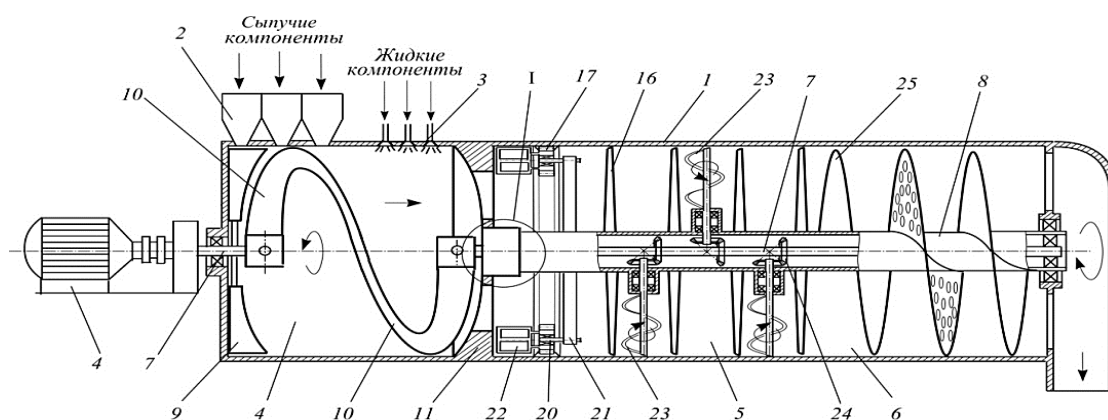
Смеситель с Z-образным рабочим органом. Общий вид. 1 – корпус; 2 – загрузочные патрубки; 3 – форсунки; 4–6 – камеры; 7, 8 – быстроходный и тихоходный валы; 9 – очищающие лопасти; 10 – z-образные лопасти; 11 – опора; 16 – конусообразные лопасти; 20 – ось; 21 – стойка; 22 – рамные мешалки; 23 – спирали; 24 – конические зубчатые колеса; 25 – шнек
